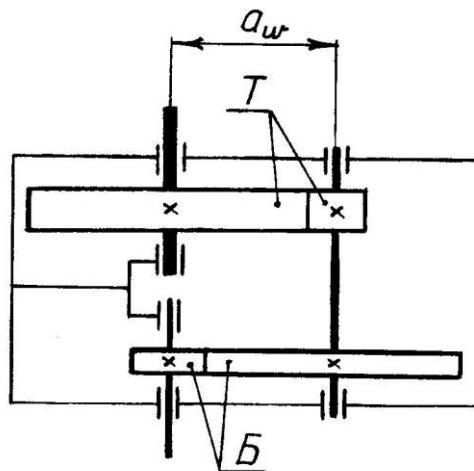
Схема цилиндрического соосного двухступенчатого редуктора:
